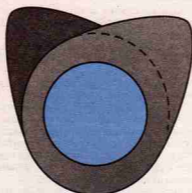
Положение кулачков первого цилиндра при укладке распределительного вала в опоры головки цилиндров
